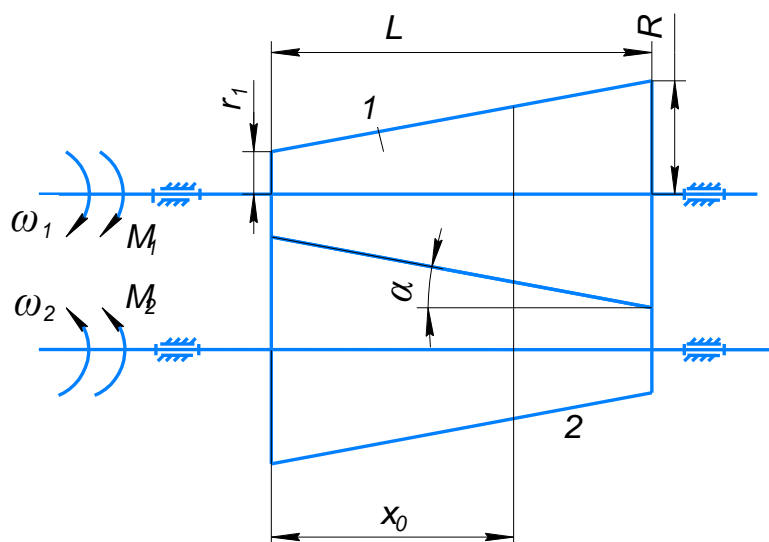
Схема механизма фрикционной передачи с параллельными валами
